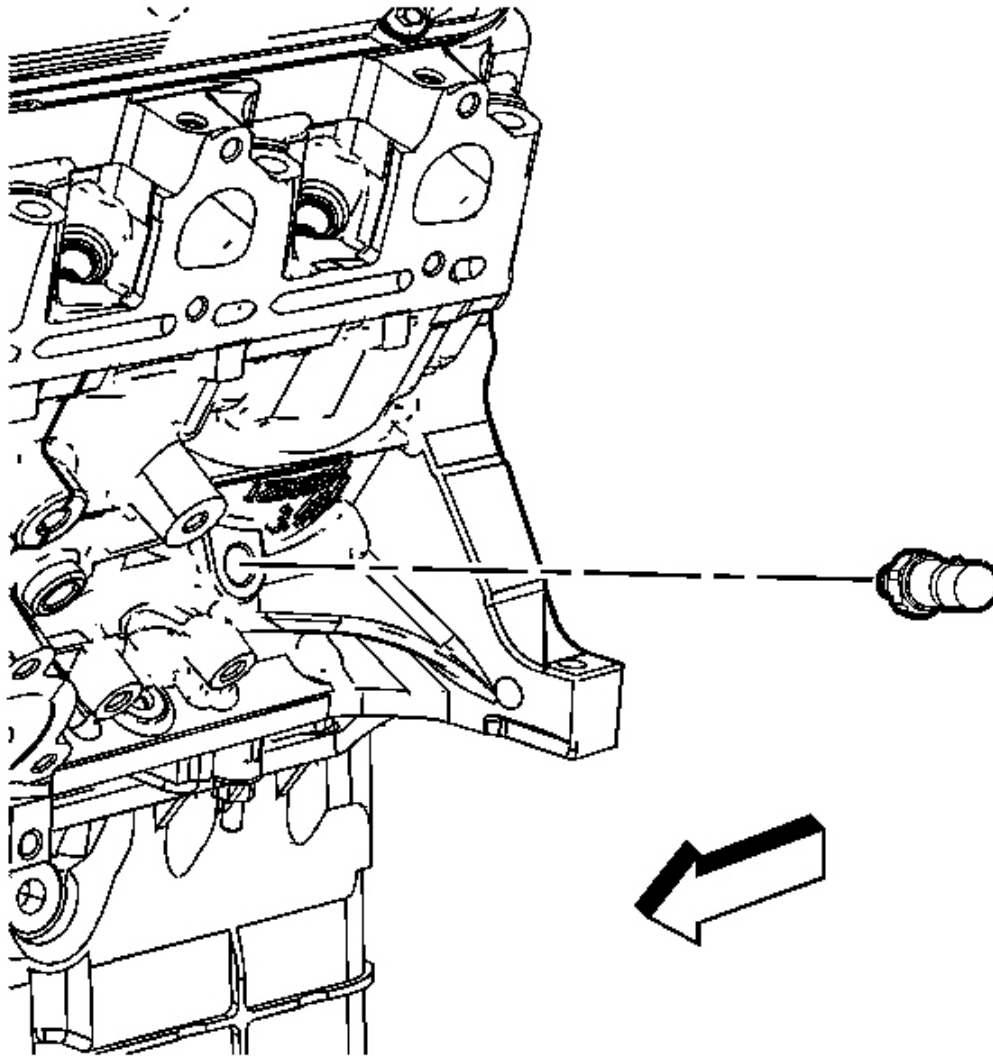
Vista del bloque del motor del enchufe, motor y transmisión Calentador del bloque posicionamiento, Clavijas Cortesía de General Motors Corp.
